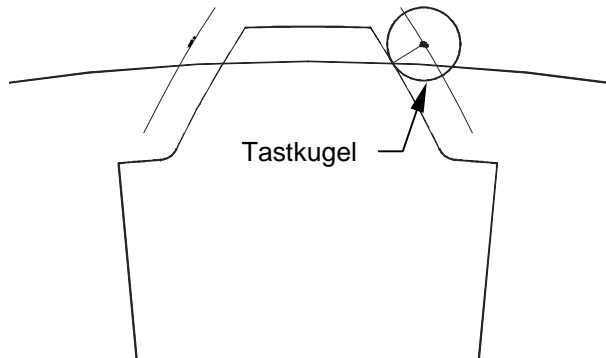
Zahn mit Tastkugel, verschobener Flanke und zugehörigem Messkreisradius in ProE
